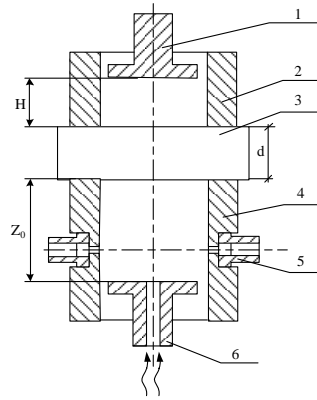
Конструкція вимірювального перетворювача з двома налагоджувальними поршнями і внутрішнім розташуванням зразка. 1, 6 – налагоджувальні поршні; 2, 4 – частини складеного резонатора; 3 - зразок; 5 – підводжуючі хвилеводи.
